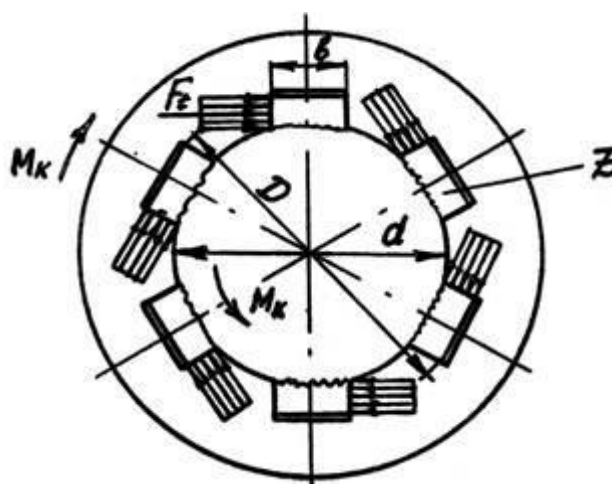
Розрахункова схема шліцевого з'єднання
